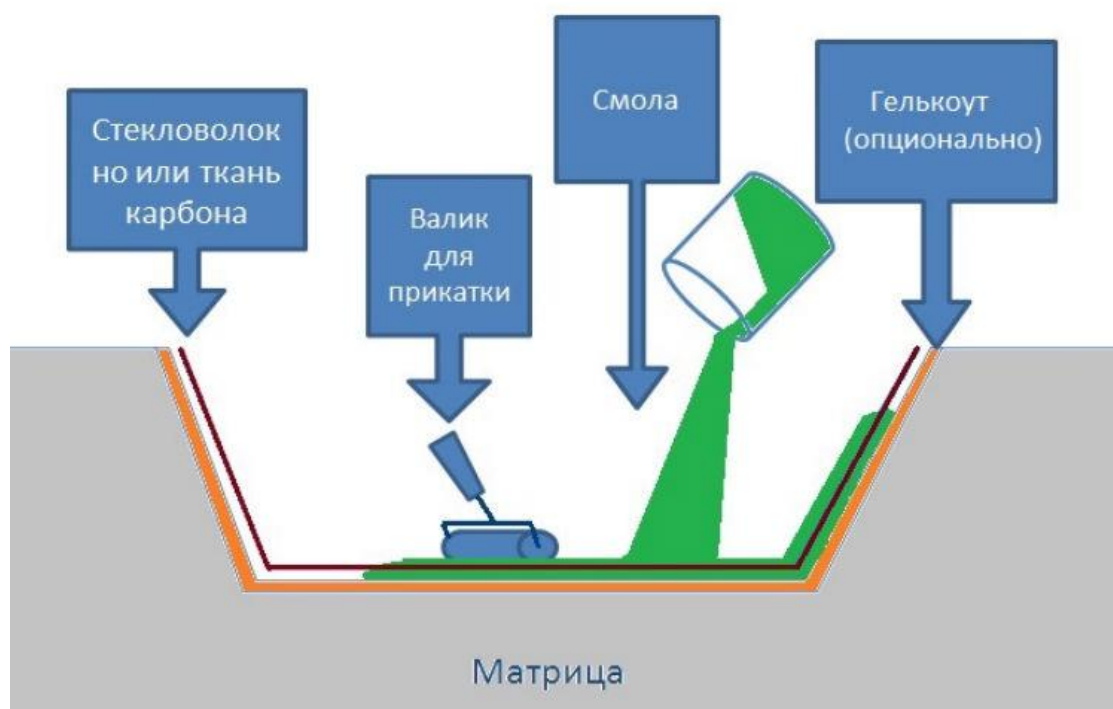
Схема ручного формования стеклопластикового изделия.
